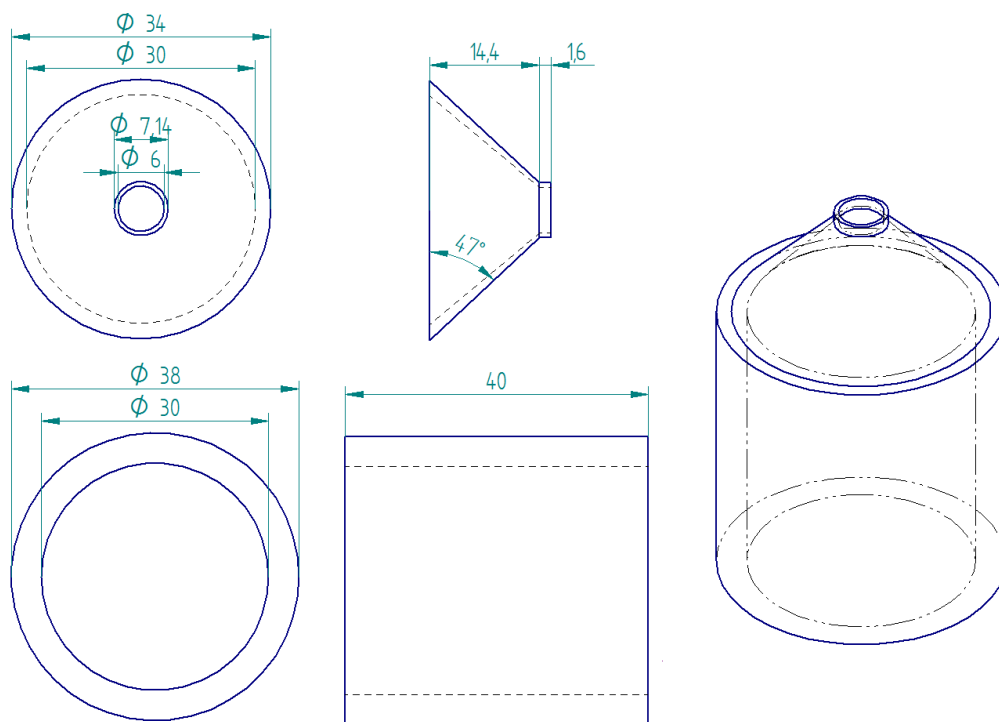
CAD Zeichnungen des Ringmagnets mit Polkappe
